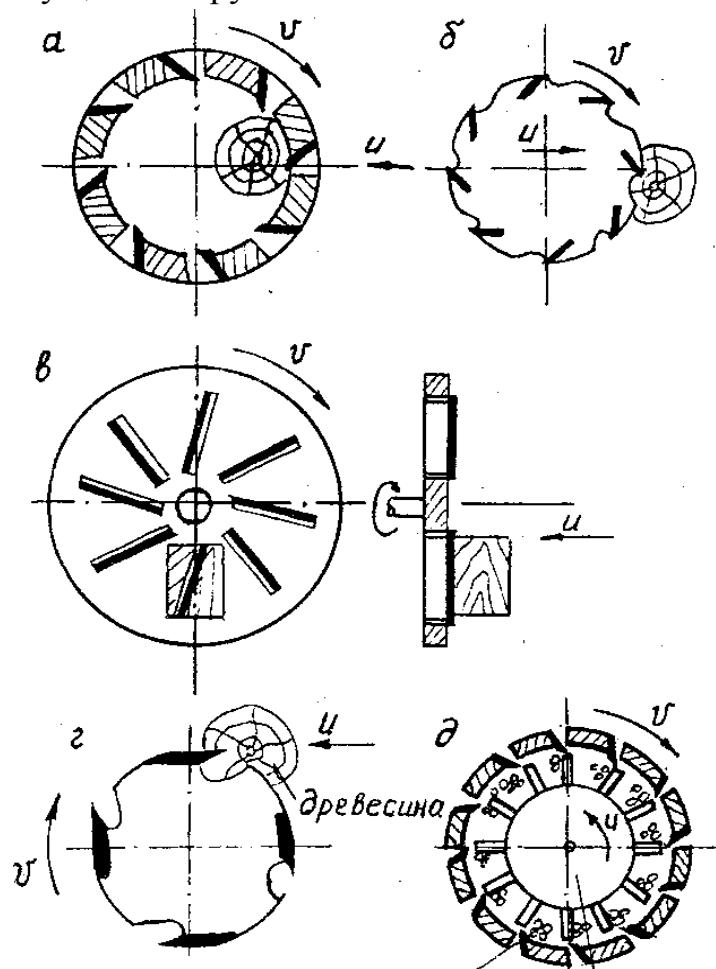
Принципиальные схемы стружечных станков различного типа: а – чашеобразного; б – фрезерного; в – дискового; г – с ножевым валом; д – центробежного
